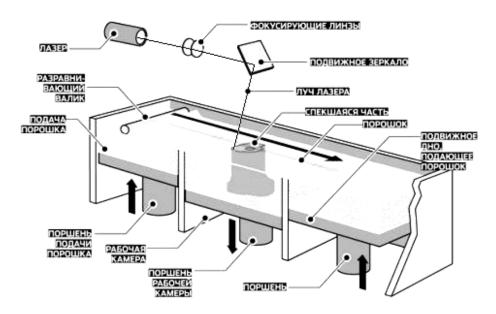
Схема установки для лазерного спекания порошков с порошковой камерой
